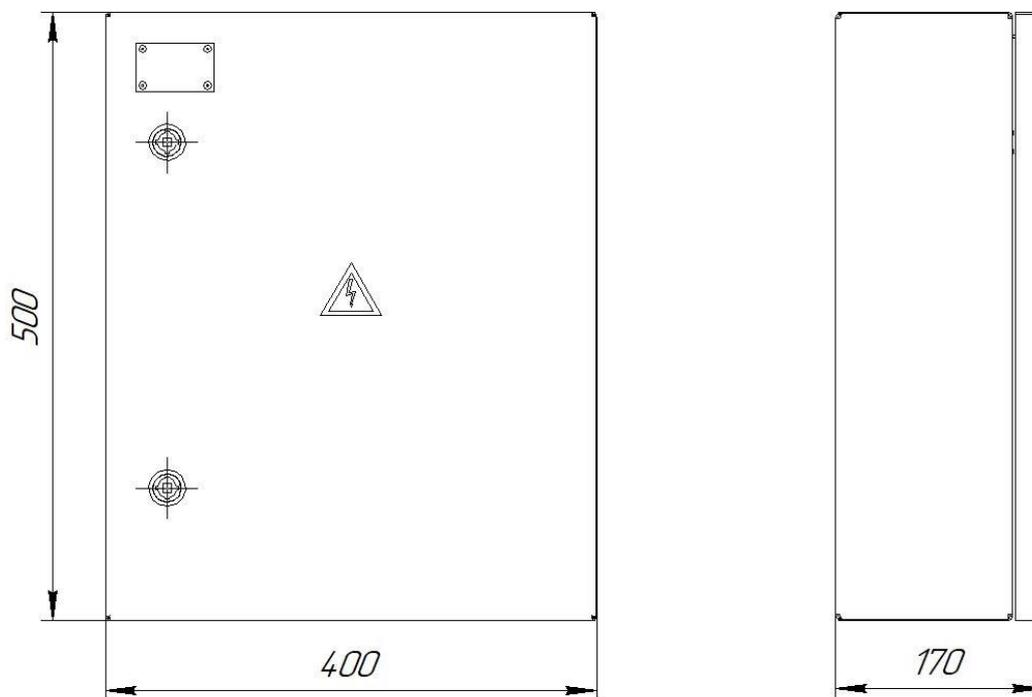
Габаритные размеры аудиоусилителя БА150
